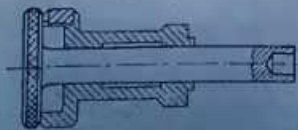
Направляющая оправка ЛМ9690-160 для установки шестерни-водила на ось
